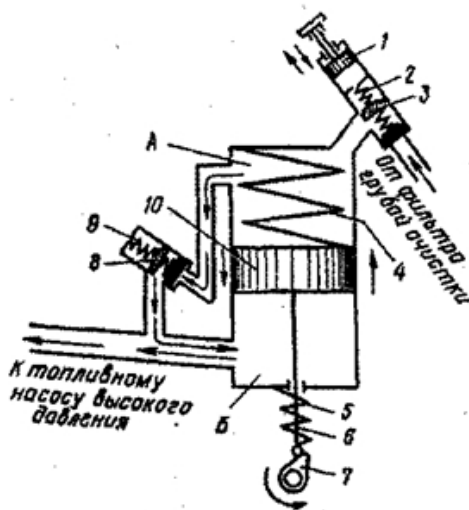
Схема работы топливного насоса низкого давления и топливоподкачивающего насоса А и Б - полости; 1 - поршень топливоподкачивающего насоса; 2 - пружина клапана; 3 - впускной клапан; 4, 5, 9 - пружины; 6 - толкатель; 7 - эксцентрик; 8 - нагнетательный клапан; 10 - поршень насоса низкого давления.
